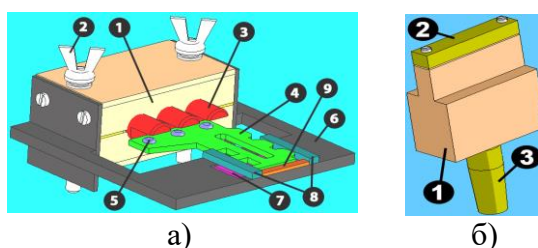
Приспособление (а) и электродный узел (б) для заводской сборки и сварки пакетных соединений засовов замков
